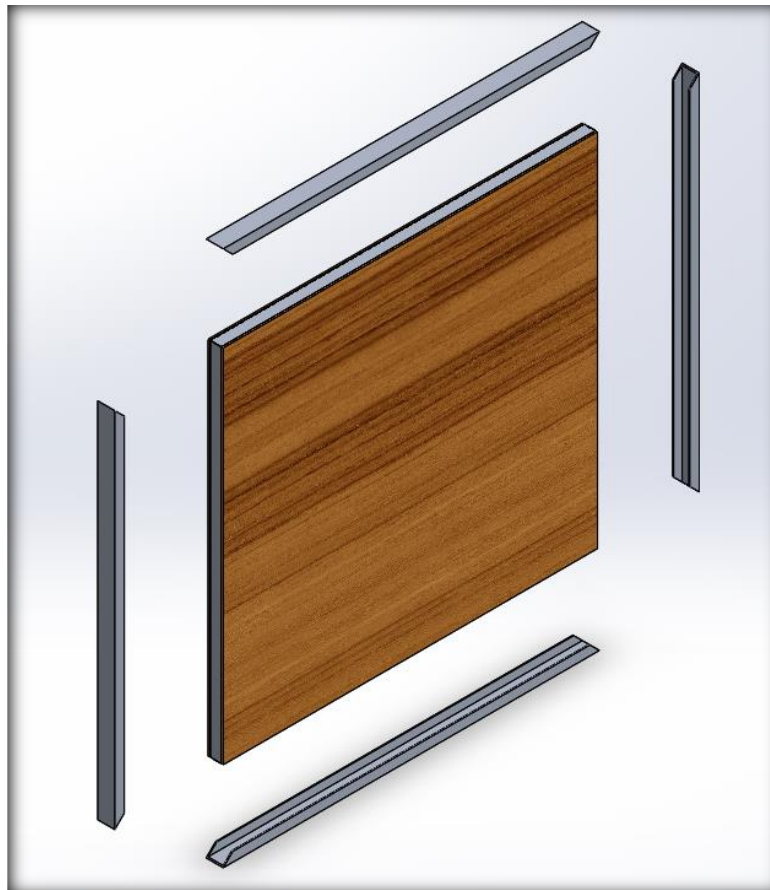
Vista extruida de ensamblaje de perfiles en U con el conjunto del cerramiento
